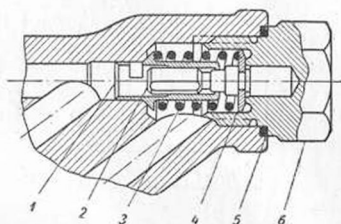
Рабочий клапан хода отдачи: 1—пробка; 2—ствержень клапана; 3—пружина; 4—шайба стержня; 5—алюминиевая шайба; 6—пробка.
